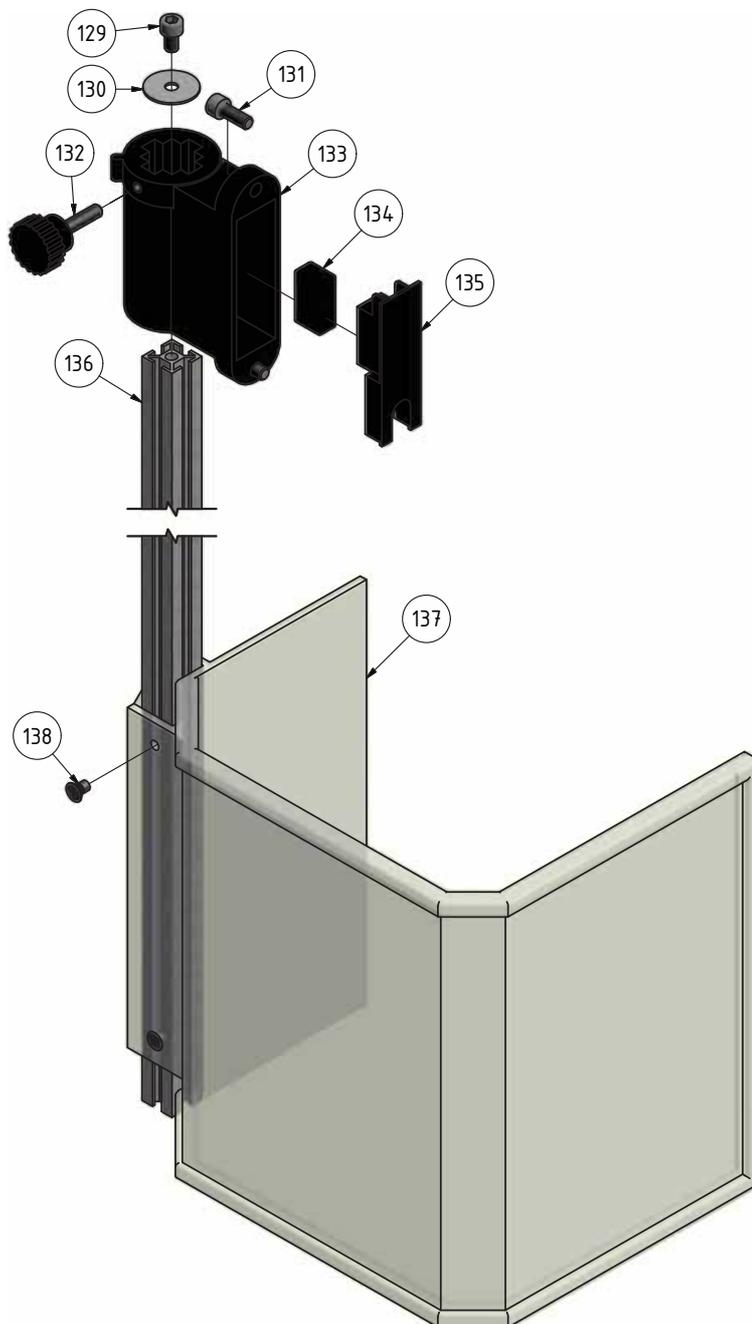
Bohrfutterschutz - Drilling chuck protection
